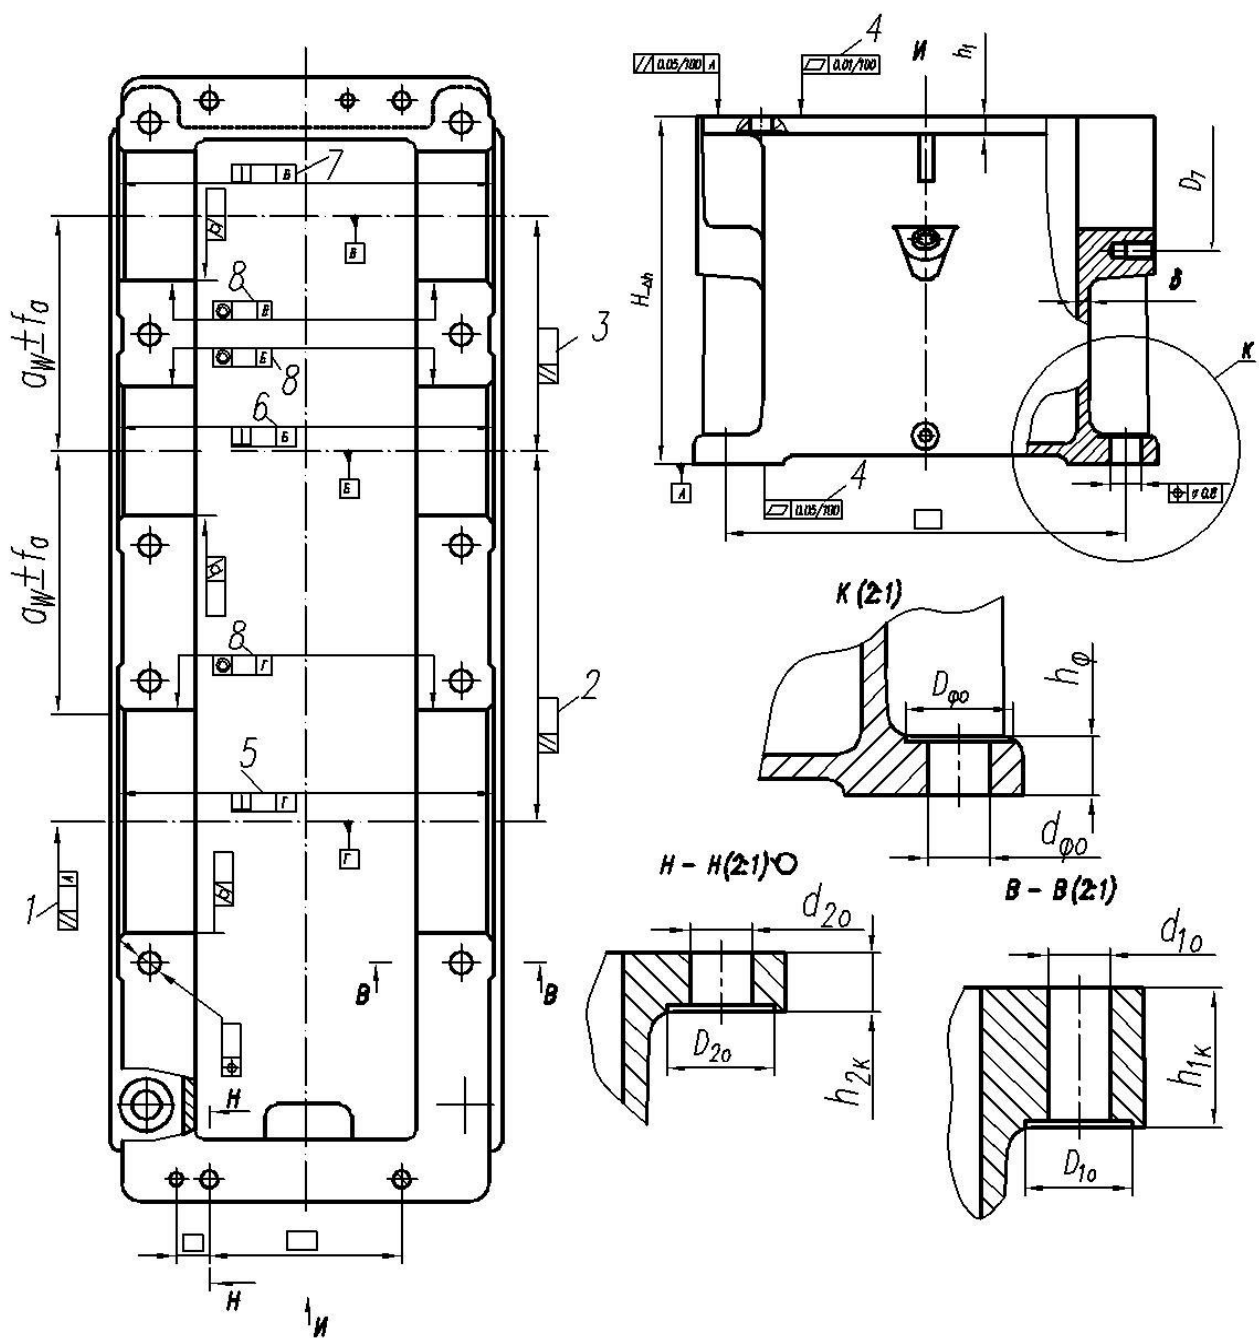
Размещение обозначений допусков форм и расположения поверхностей на чертеже основания корпуса
